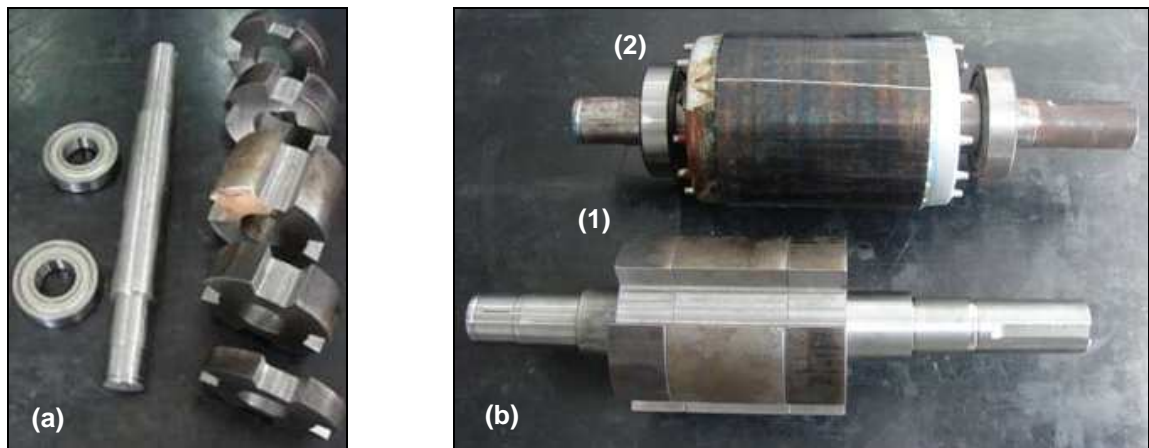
Componentes (a) e pré-montagem do rotor (b-1)
